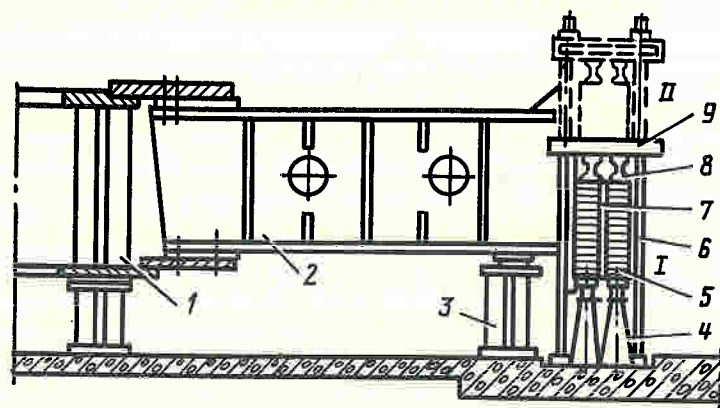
Сборка обода с опрессовкой гайковертами при помощи специального опрессовочного приспособления:
